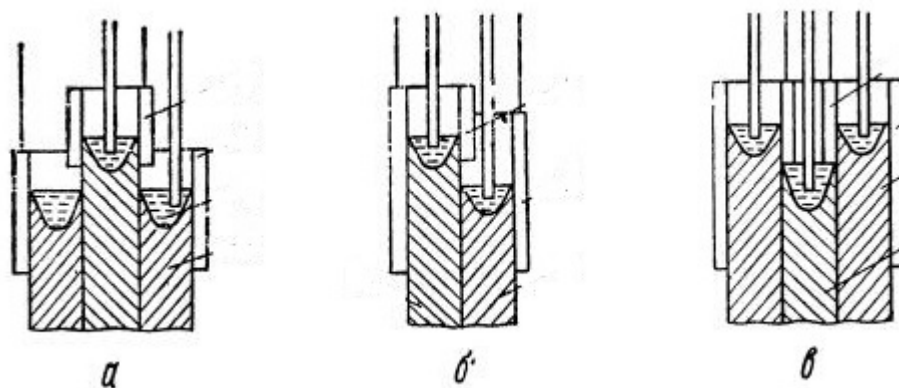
Схема безперервного литва біметалевих та поліметалевих тришарової (а); двошарової (б); двошарової циліндричної (в) заготовок [1]
